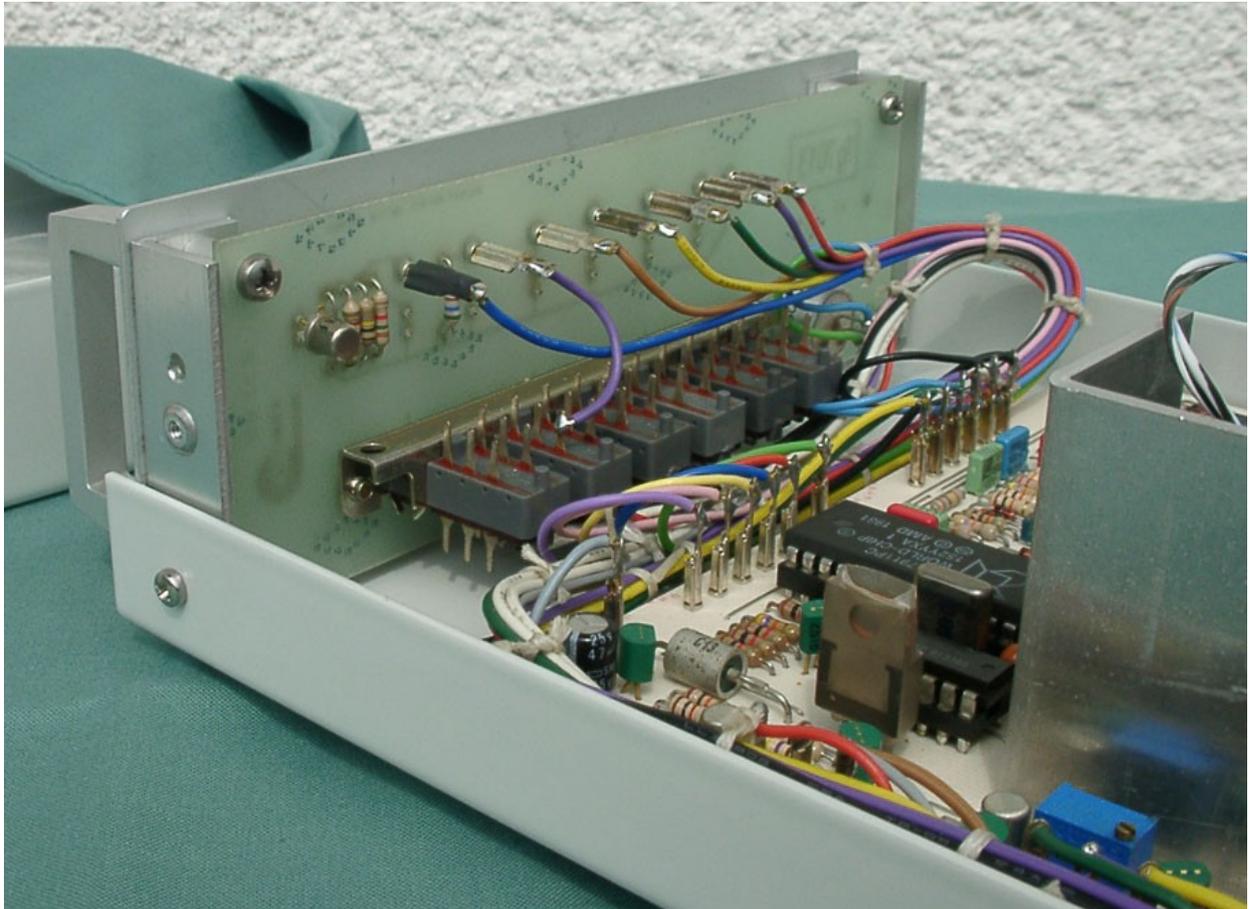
Ein fertiges, geöffnetes Gehäuse; auch der Kabelbaum ist zu erkennen
